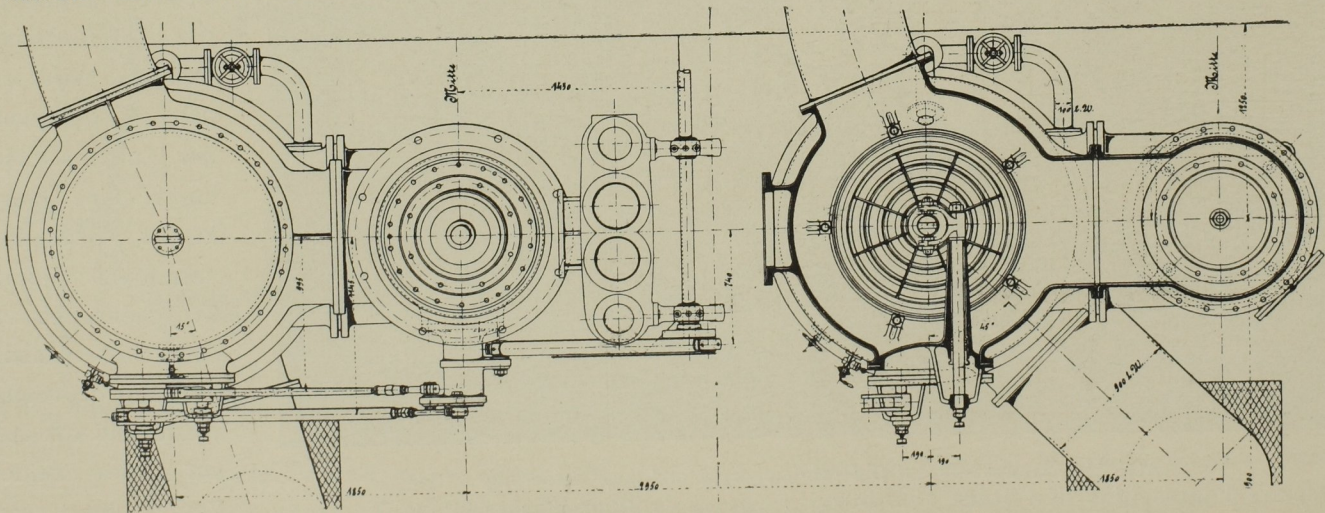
Grundriss und Schnitt der Pumpen. Massst. 1 : 45.
